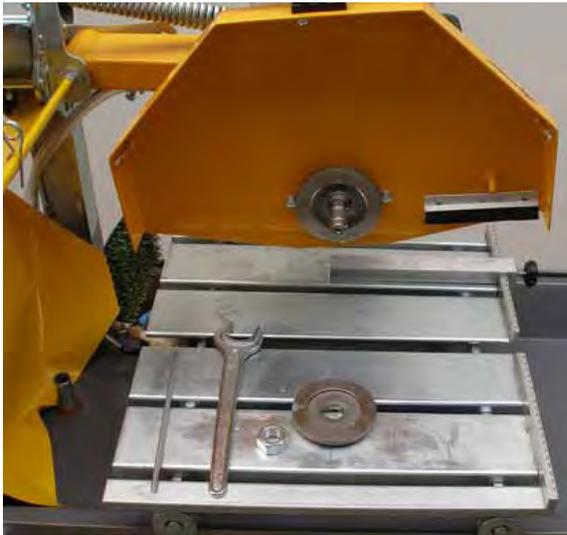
, Schneidwellen-Mutter und Blatt-Druckflansch demontiert
